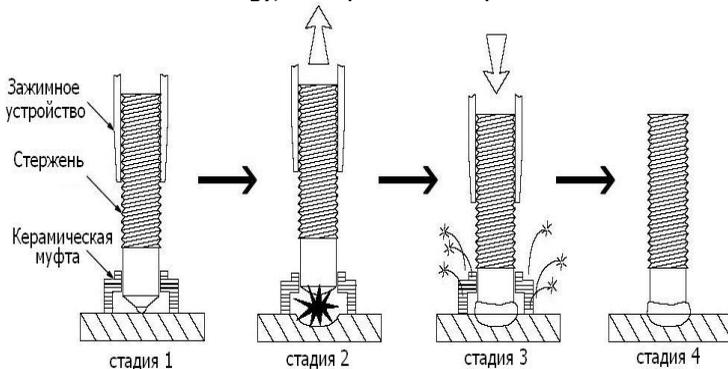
Схема процесса с принудительным растяжением дуги (Drawn arc stud welding).
